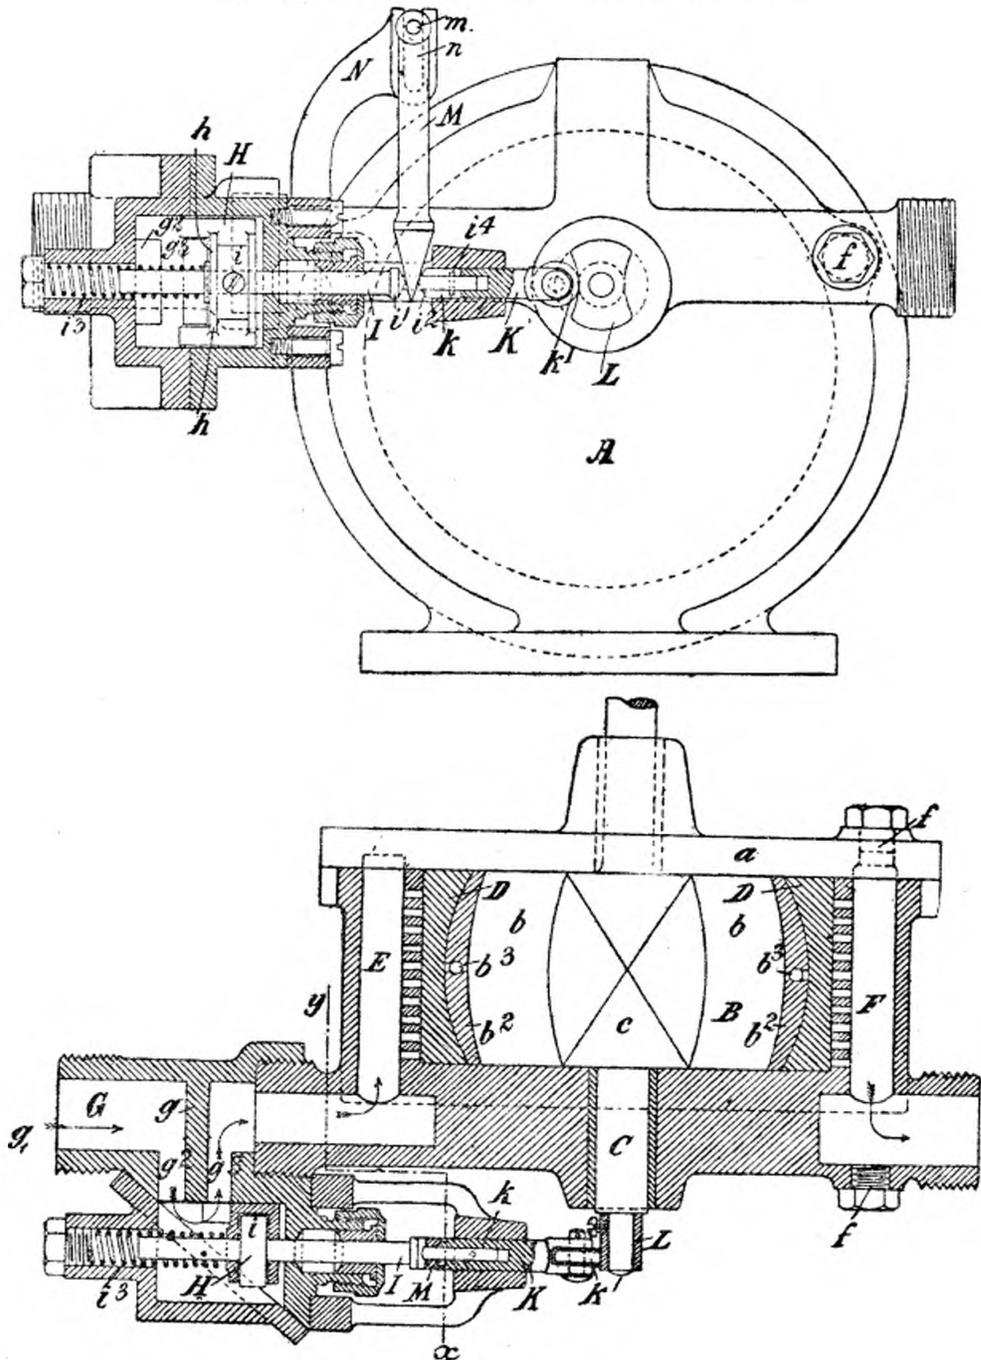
et 329. Vue de faces, et coupe diamétrale par le régulateur.
